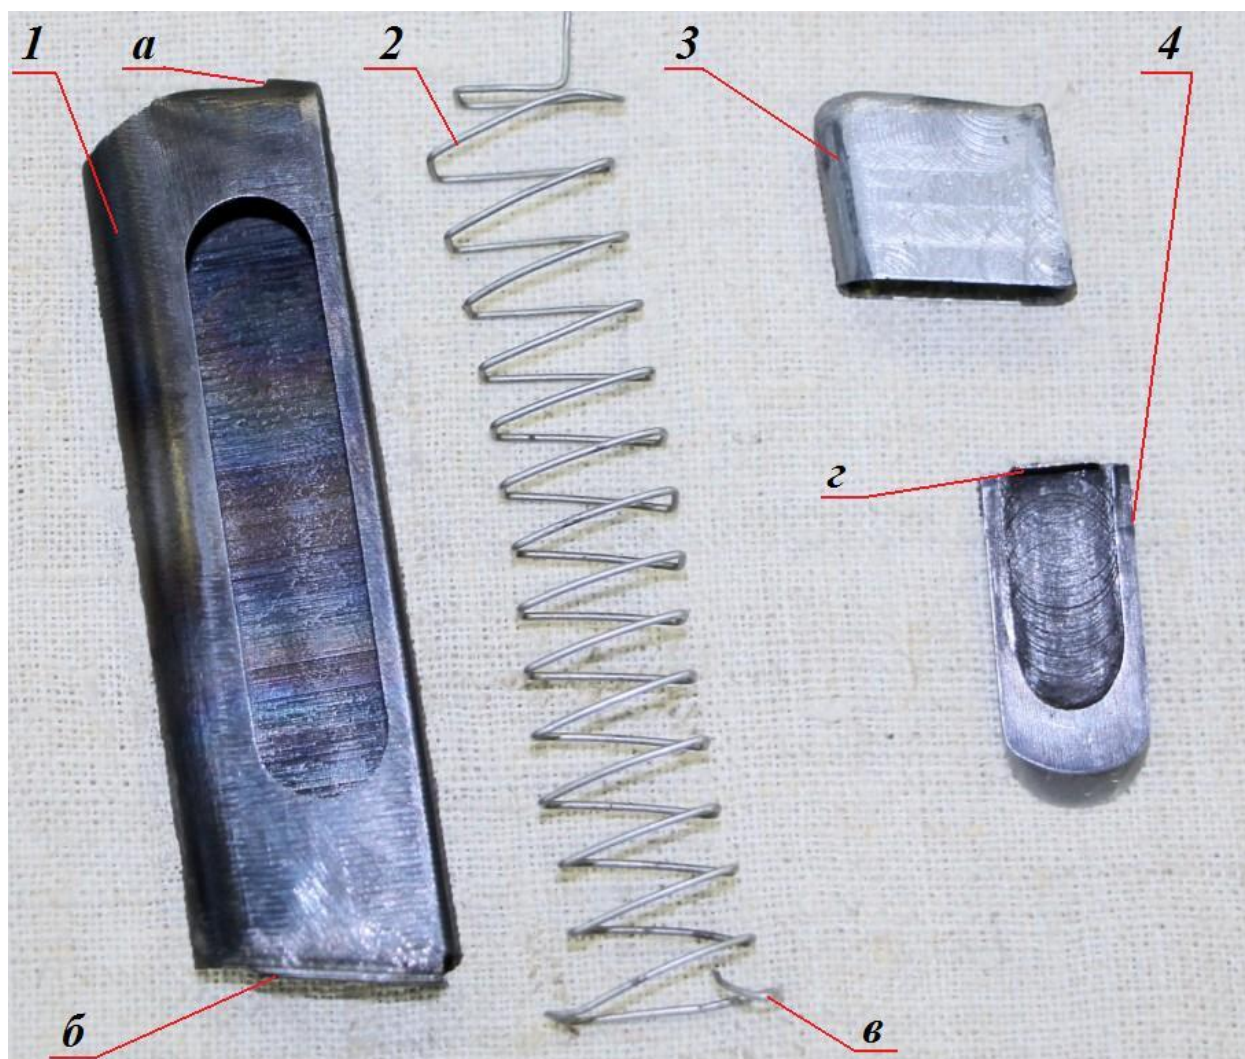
Магазин «пистолета гражданского типа» в разобранном виде. 1 — коробка (а — отражающий выступ, б — направляющие для крышки); 2 — пружина подавателя (в — уступ); 3 — подаватель; 4 — крышка (г — выступ).
